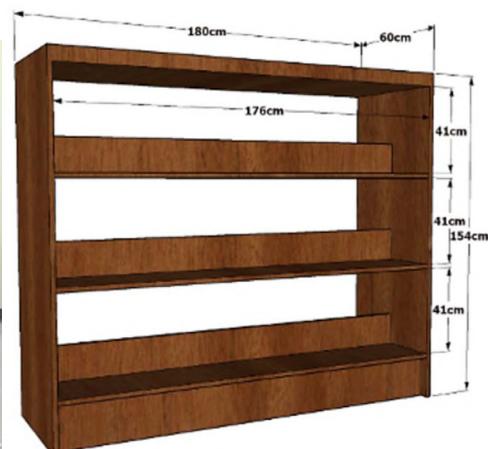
Rak buku tipe B di ruang perpustakaan umum lamongan
